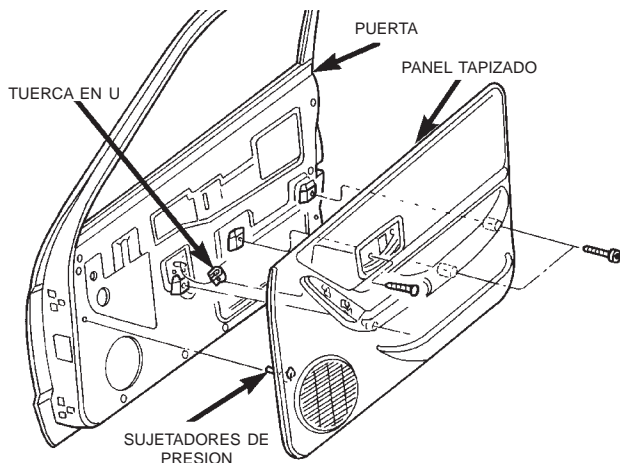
Desmontaje e instalación del panel tapizado de la puerta delantera - Elevalunas eléctrico
